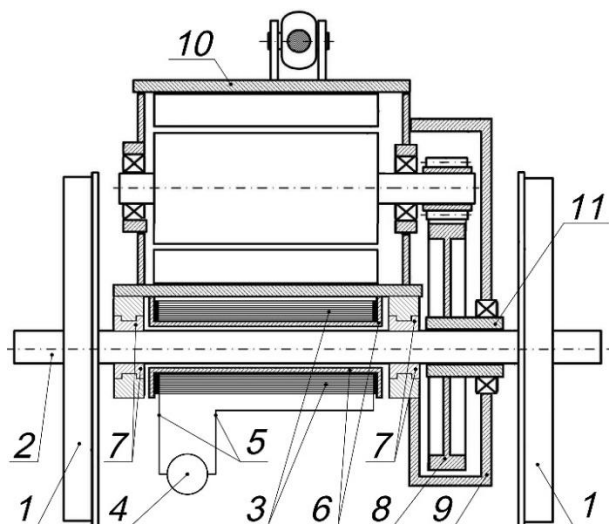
Схема расположения обмотки индуктора между моторно-осевыми подшипниками
